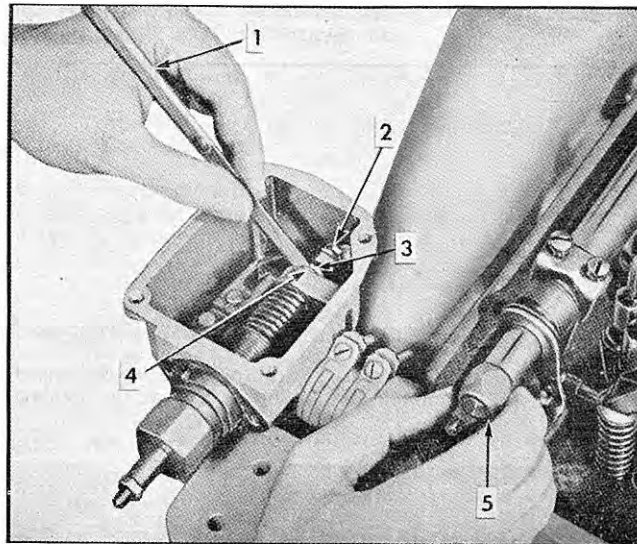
Réglage du jeu - Jauge n° J 3172
